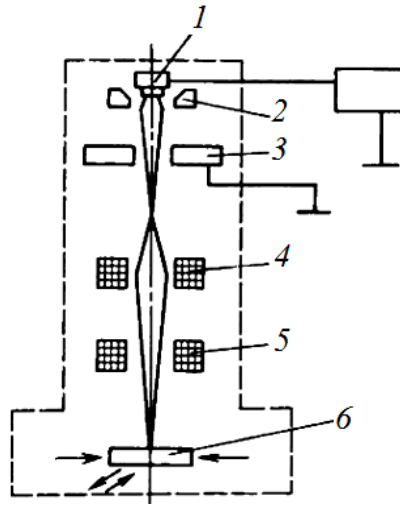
Схема установки для электронно-лучевой сварки
